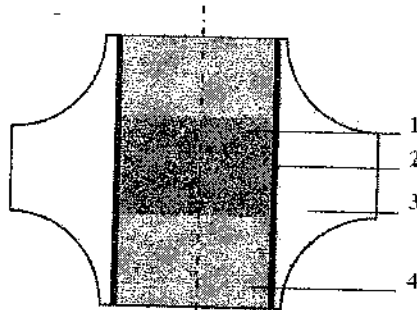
Вид контейнера высокого давления со спекаемой заготовкой: 1 – заготовка; 2 – трубчатый нагреватель, 3 – контейнер, 4 – теплоизолирующие заглушки
